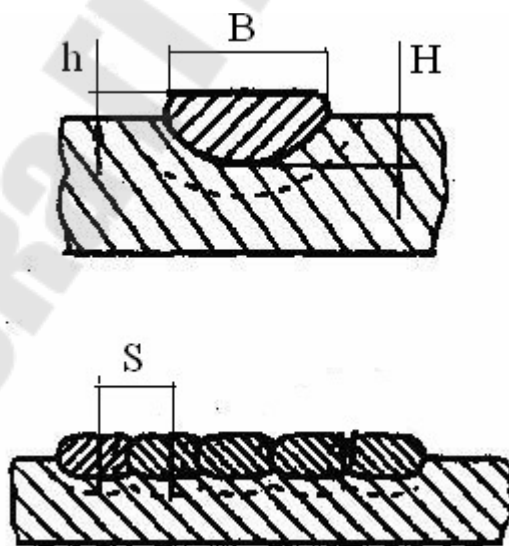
Способы наложения слоёв при наплавке: В – ширина валика; h – высота наплавки; Н – глубина проплавления; S – шаг наплавки
